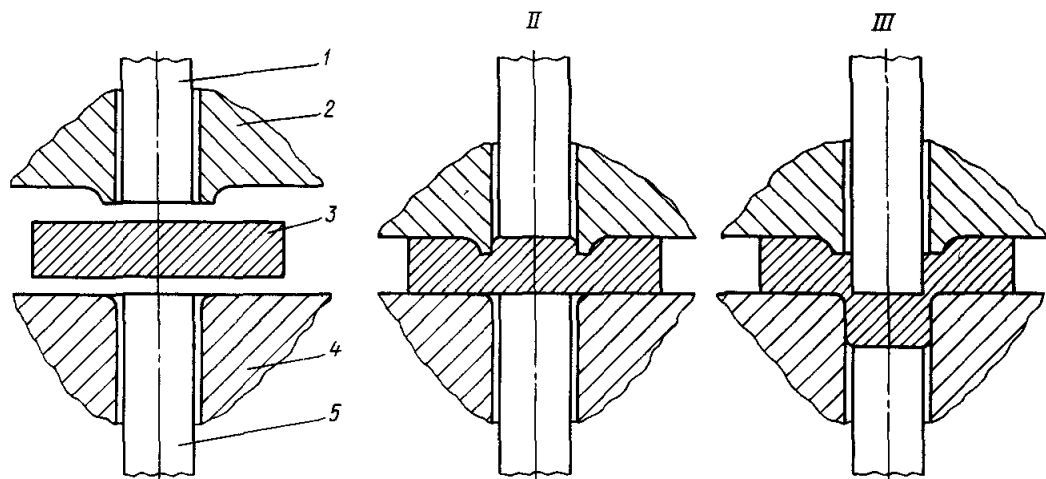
Схема способу реверсивного чистового вирубкування:
